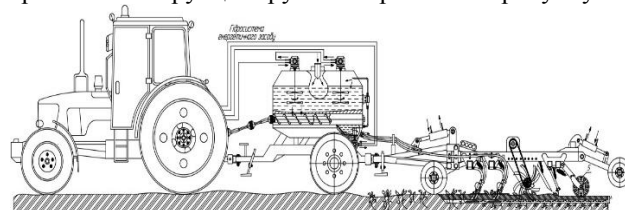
Загальний вигляд машинно-тракторного агрегату для технології Strip-till
